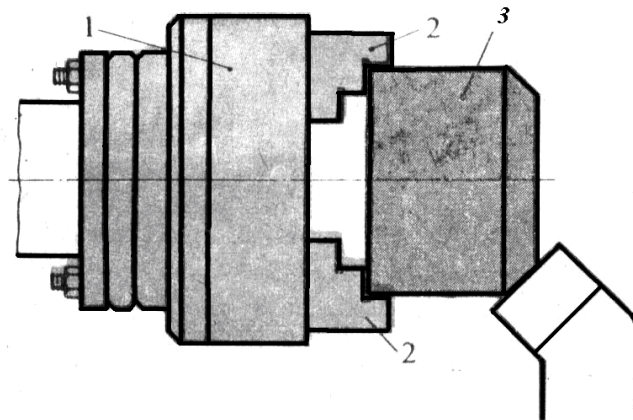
Закріплення заготовки в зворотних кулачках патрона:
